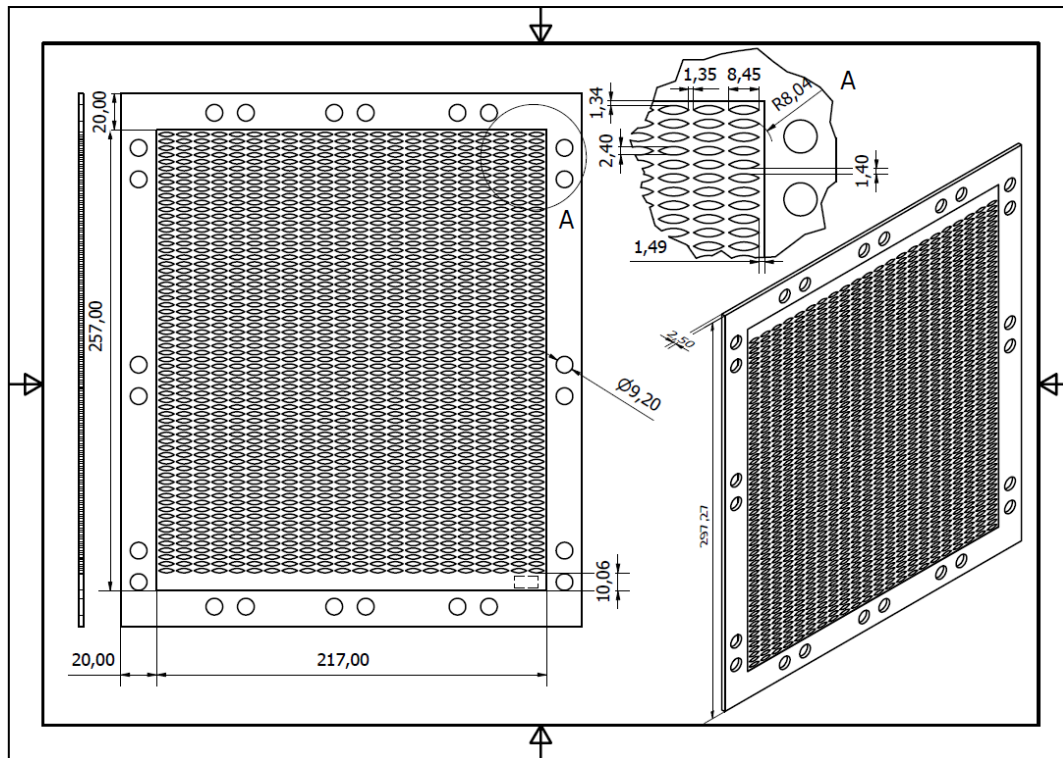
Diseño final de placa muestral (cotas en mm) (Fuente: Elaboración propia).
